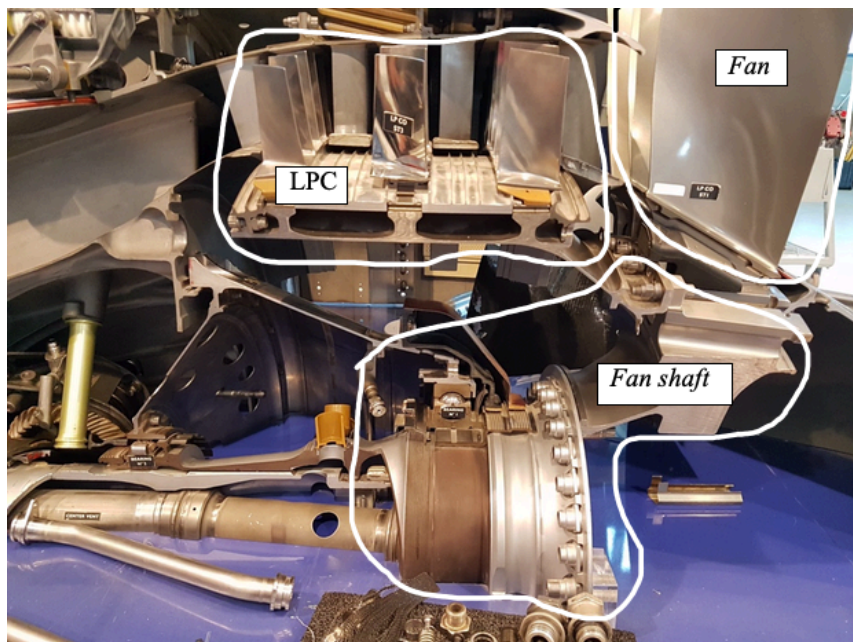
Montagem do compressor de baixa pressão (LPC) à fan shaft juntamente com a fan
